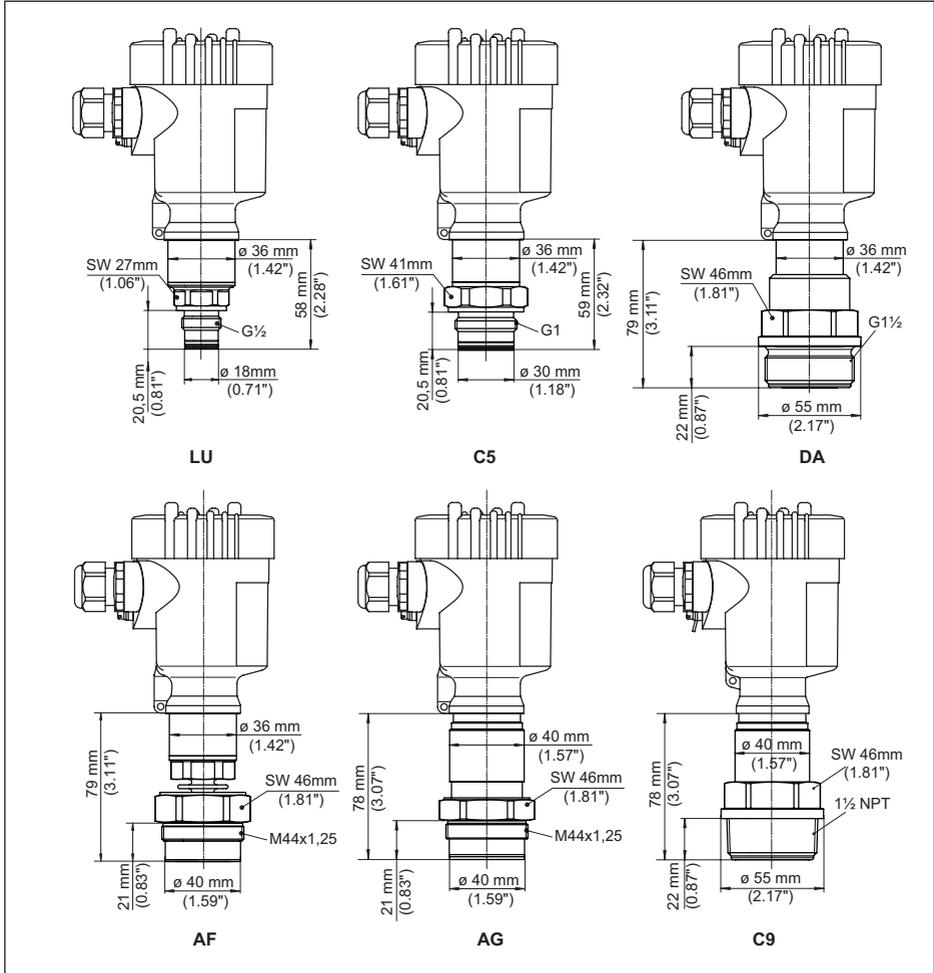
VEGABAR 83, Gewindeanschluss frontbündig
